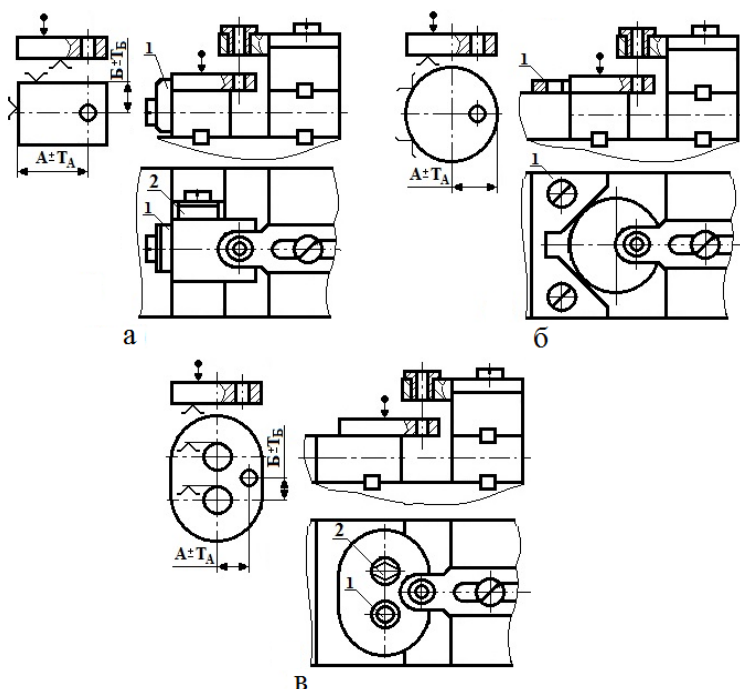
Операционные эскизы заготовок и схемы УСП для их обработки
